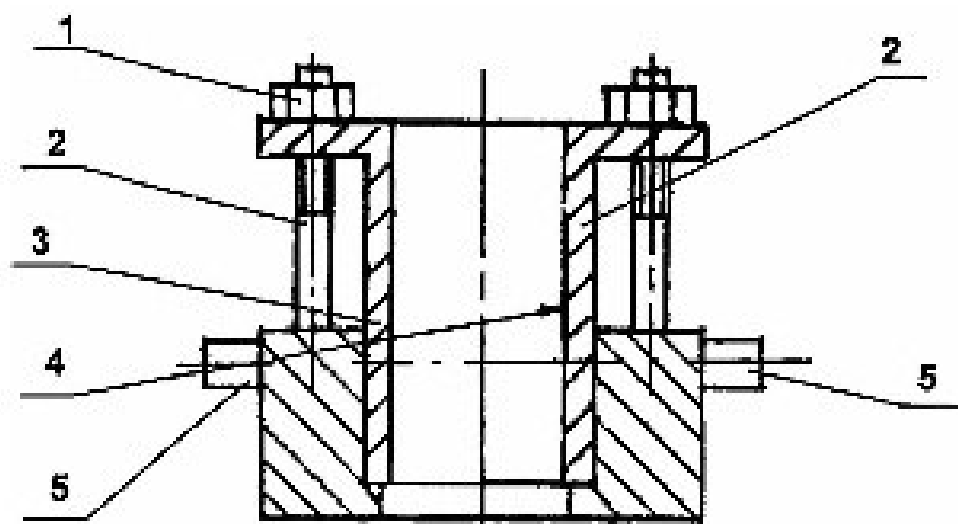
Схема крепления гильзы цилиндра в съемной части приспособлении-спутнике
